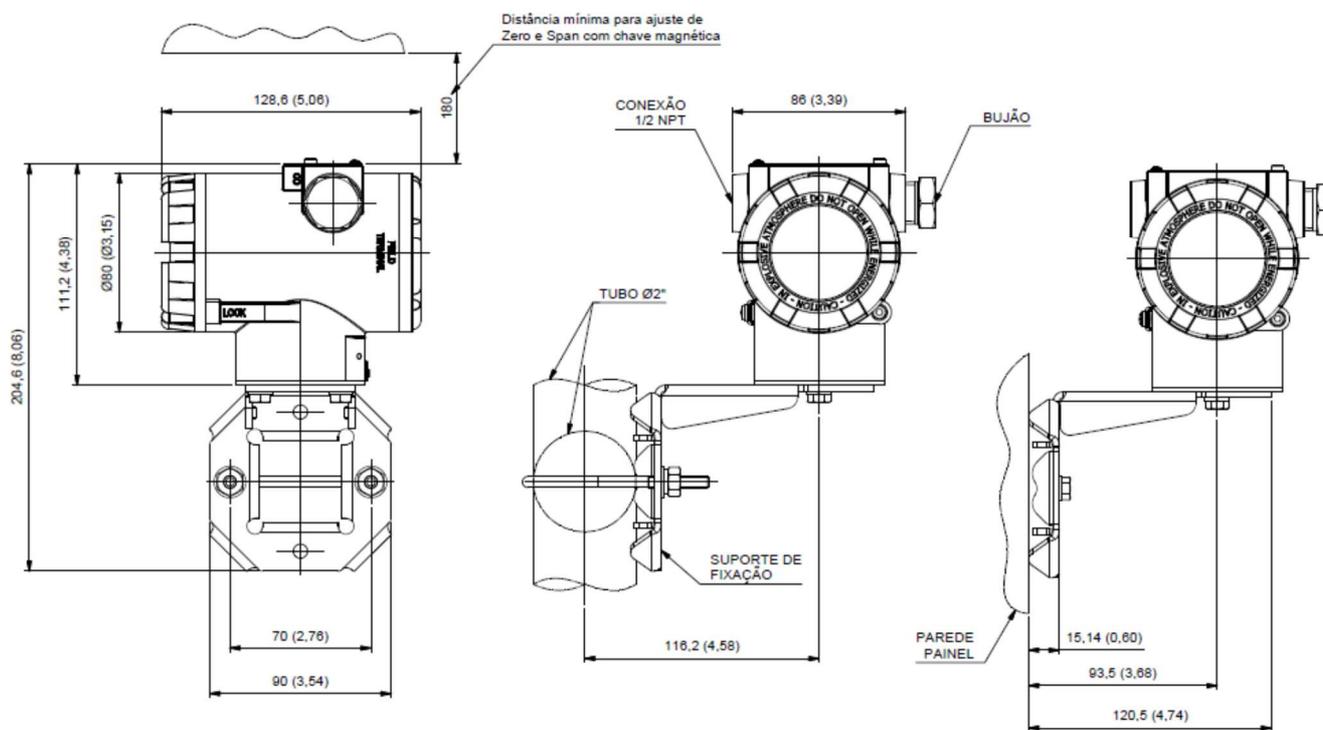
Desenho dimensional e esquema de montagem do VTT10-FH.
